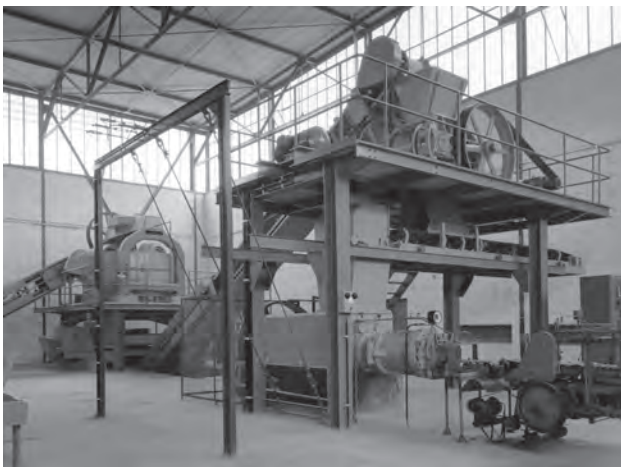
Anlage mit Kollergang, Walzwerk und Strangpresse, um 1960
